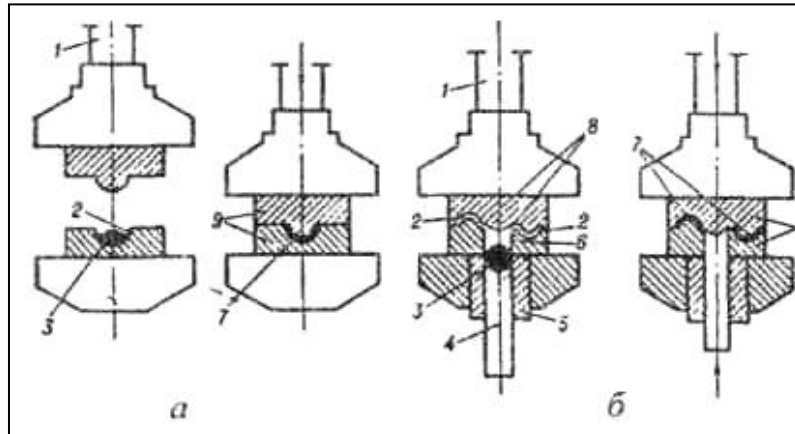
Схема формирования изделий из реактопластов (*а* - компрессионное прессование; *б* - литьевое прессование): 1 - верхний плунжер; 2 - оформляющие гнезда прессформы; 3 - перерабатываемый материал; 4 - поршень; 5 - трансферный цилиндр; 6 - загрузочное отверстие; 7 - изделие; 8 - литниковые каналы; 9 - пресс-форма
